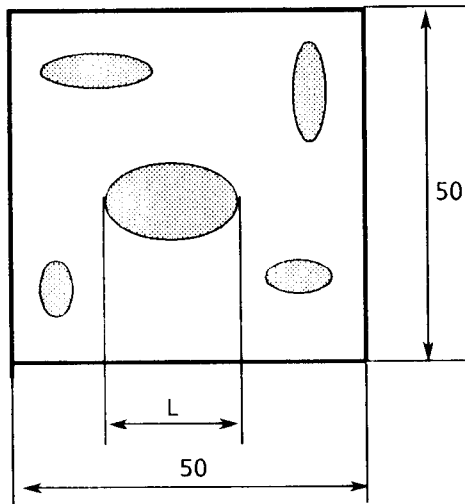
Ytliga defekter utom sprickor och vällningfel/Surface defects except for cracks and unfused chaplets
